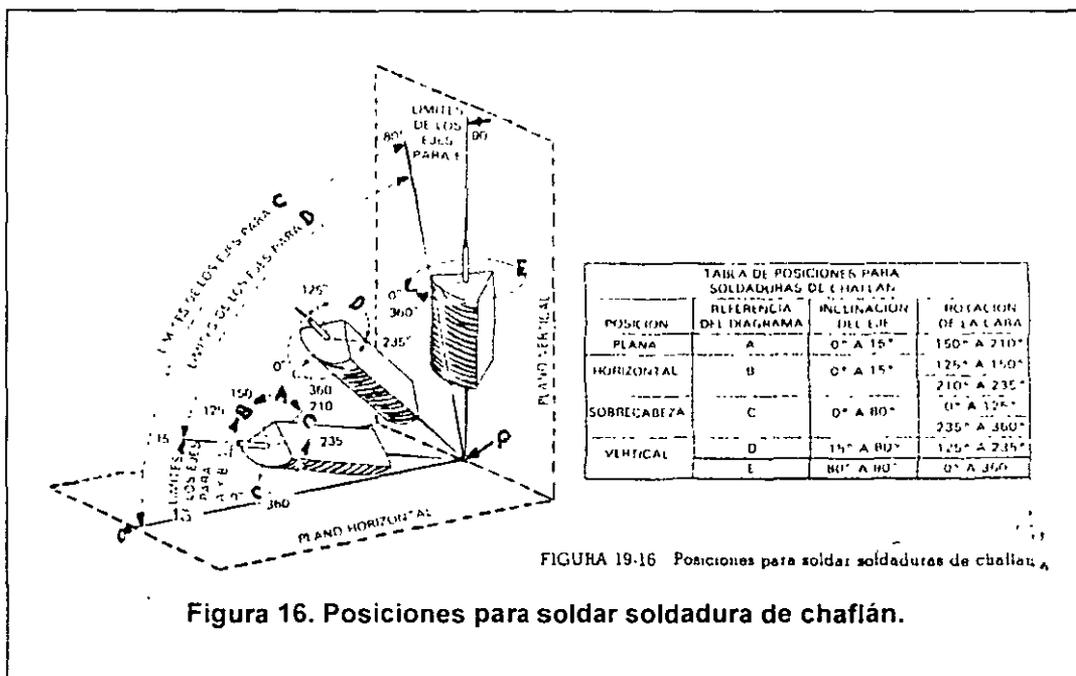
Posiciones para soldar soldaduras de chafIán.
